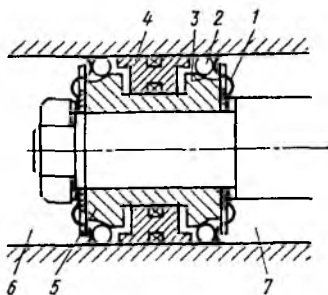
Поршень гидроцилиндра с фиксирующими устройствами
